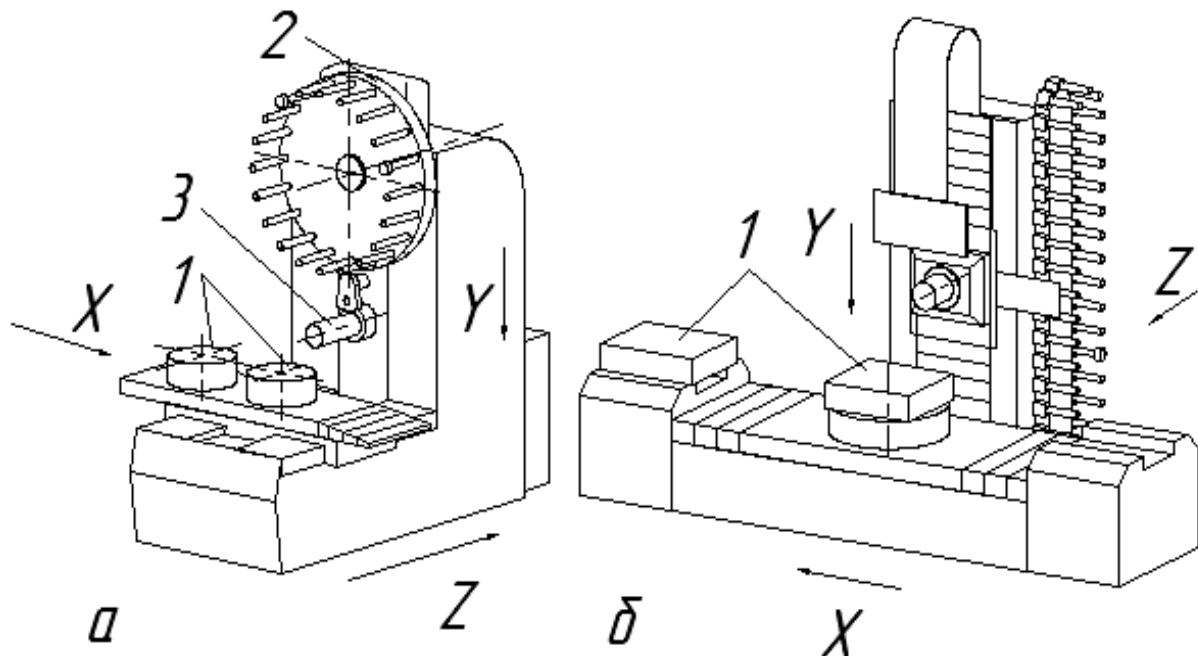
Загальний вигляд оброблюючих центрів з ЧПК:
